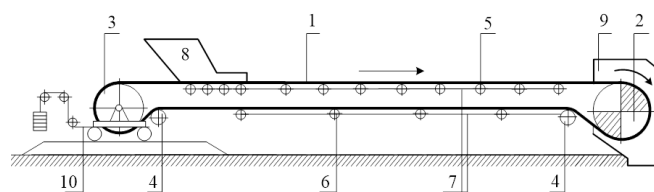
Схема горизонтального ленточного конвейера. 1-лента; 2-приводной барабан; 3-натяжной барабан; 4-отклоняющий барабан; 5-верхние роликоопоры; 6-нижние роликоопоры; 7-рама; 8-загрузочный желоб; 9-направляющий лоток; 10-натяжное устройство
